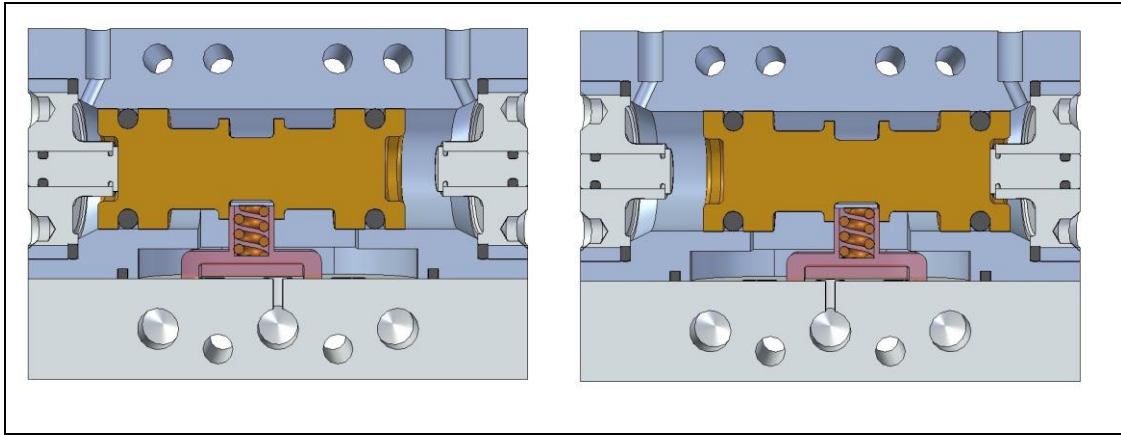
27 - Modelo de Válvula 4/2 pilotada por presión – Posiciones
